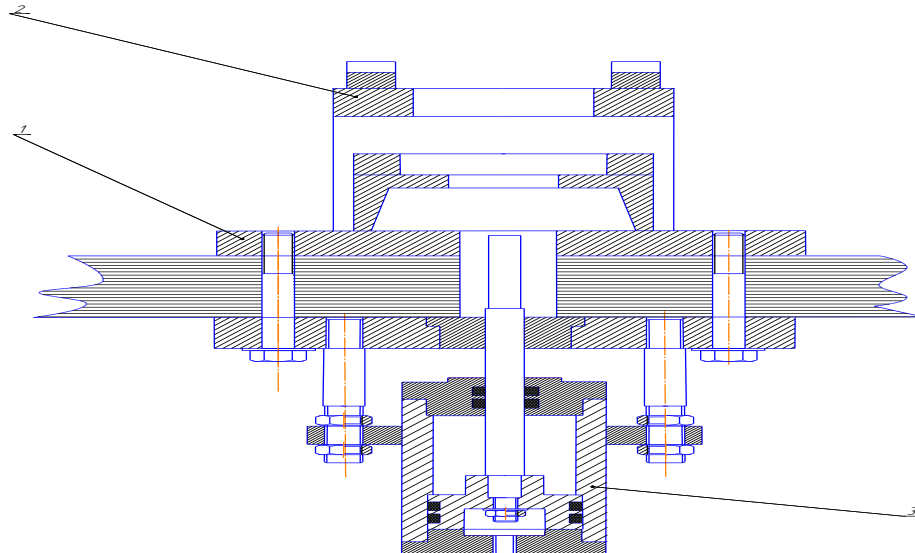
Пристосування для випресовування вала ротора з підшипника кришки генератора.
